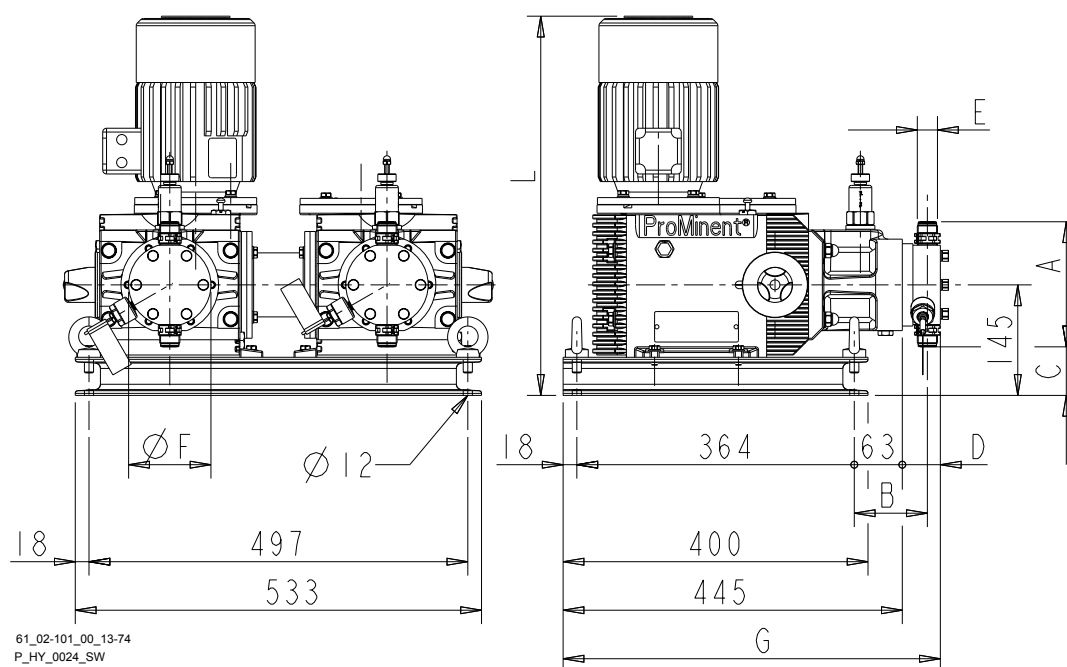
Hoja de dimensiones Hydro HP3 con accionamiento montado (HP3a E + HP3a A) - Dimensiones en mm
